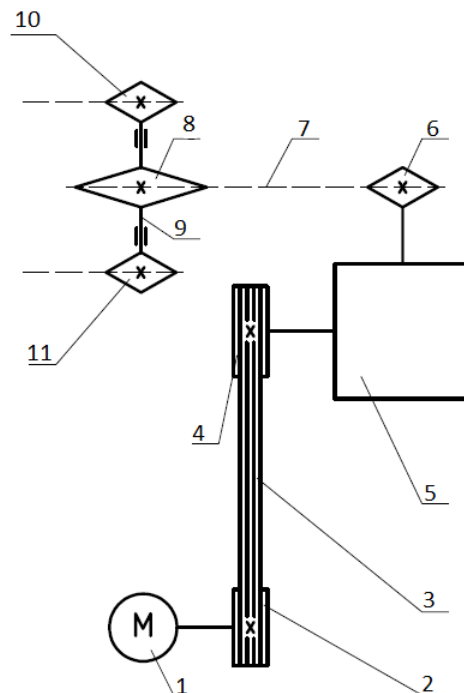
Кінематична схема привода рукавичного автомата з ланцюговою передачею
